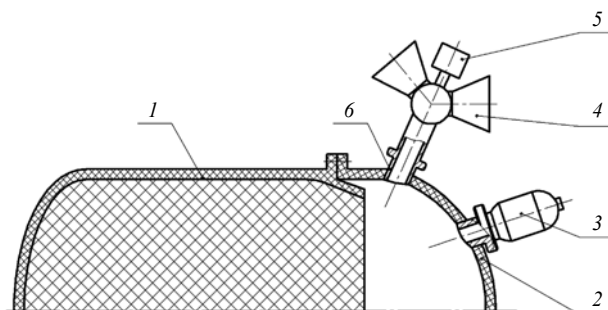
Конструктивная схема регулируемого газогенератора: 1 – топливный заряд; 2 – корпус камеры; 3 – воспламенительное устройство; 4 – сопловый блок; 5 – регулятор расхода продуктов сгорания с рулевым приводом; 6 – газоход
